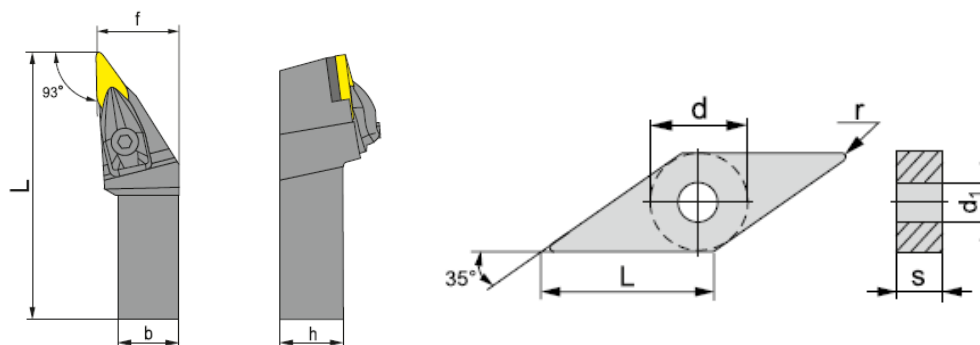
Резец для нарезания резьбы, а) державка, б) пластина
